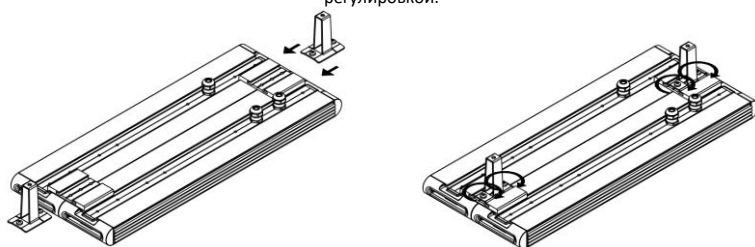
Установка крепления на соединительные планки на примере светильника Element 0,5x2 и Крепления Подвес.
